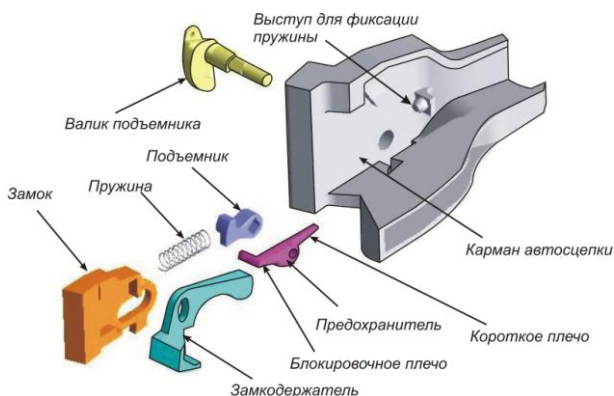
Детали механизма сцепления автосцепки СА-4
